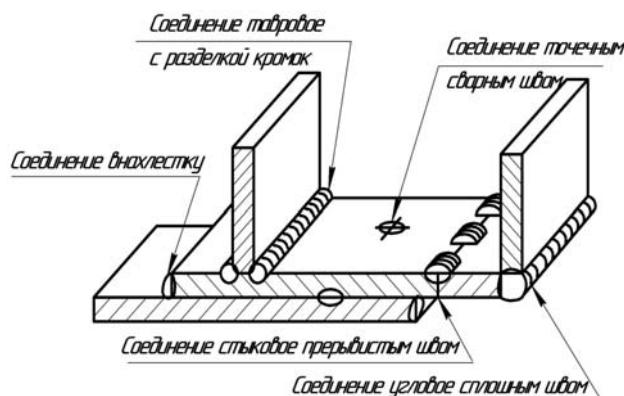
Типы сварных соединений и швов
